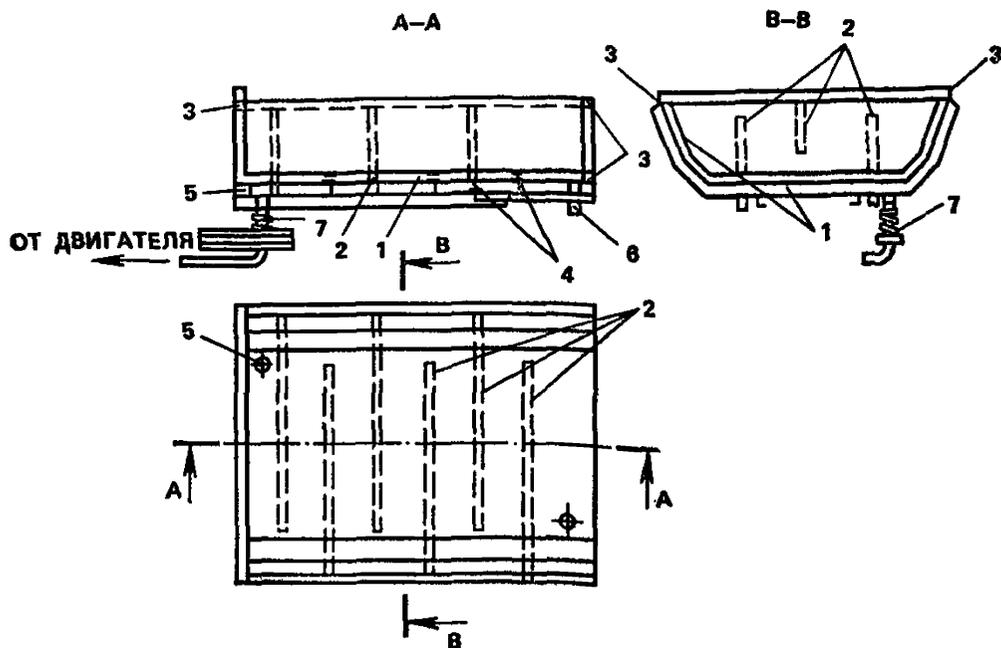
Кузов автосамосвала, оборудованный для обогрева выхлопными газами
